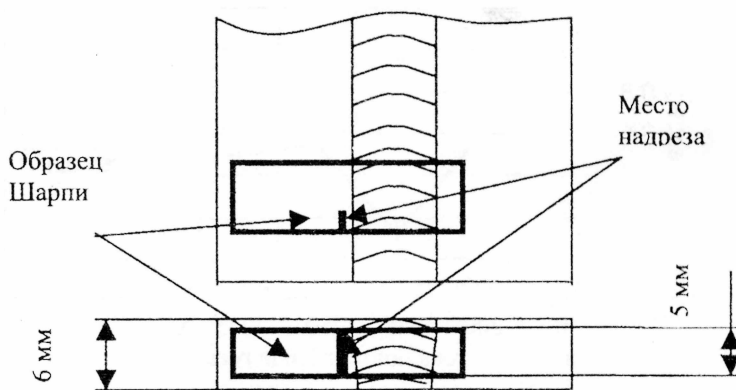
Схема вырезки образца Шарпи из сварного соединения
